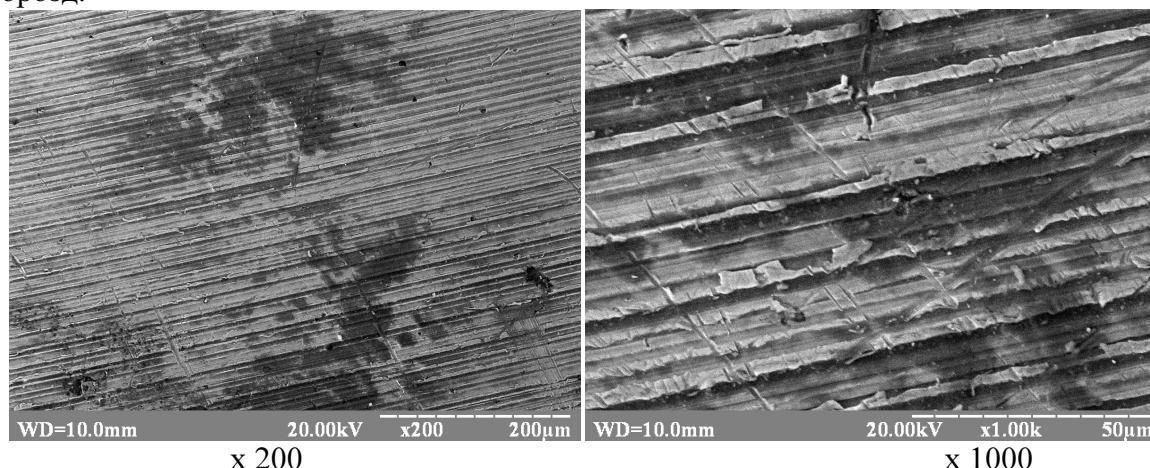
Поверхность образцов из магнитного сплава ЮН15ДК25БА после резки кругами на гальванической связке на станке ШАРМ -3
